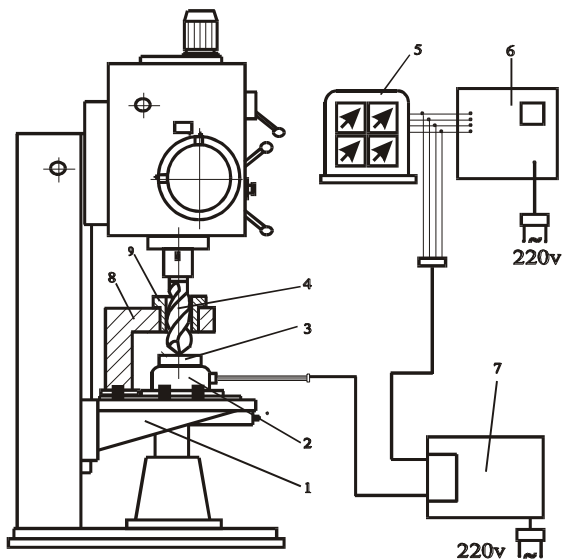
Установка для измерения силы резания при сверлении отверстий: 1) вертикально-сверлильный станок; 2) динамометр УДМ–600; 3) образец из ЛАС; 4) сверло; 5) приборный щиток; 6) осциллограф Н-115; 7) усилитель ТА – 5; 8) кронштейн; 9) кондукторная втулка.
